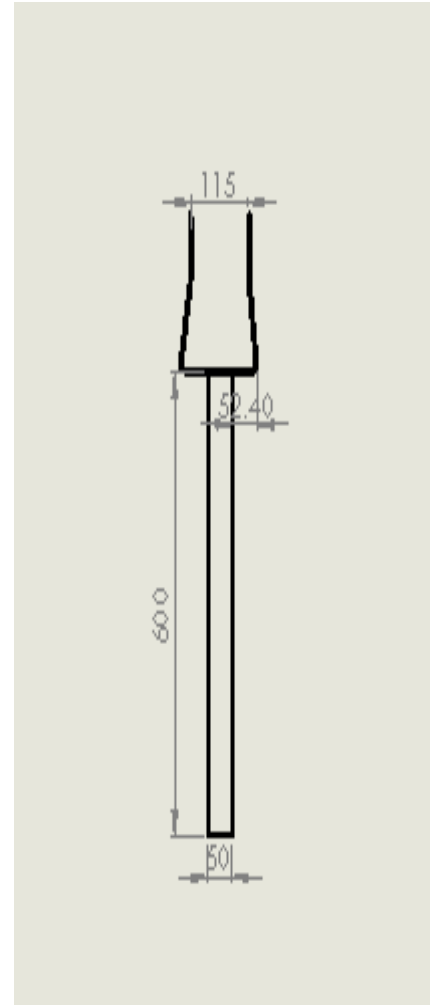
b (le dimensionnement de la jambe soudée)
